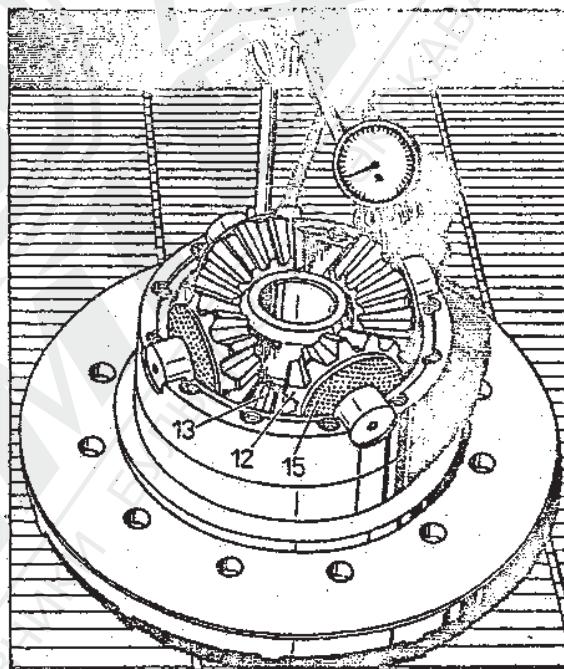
Проверка зазора между зубьями сателитов и полуосевых шестерён с помощью датчика.
